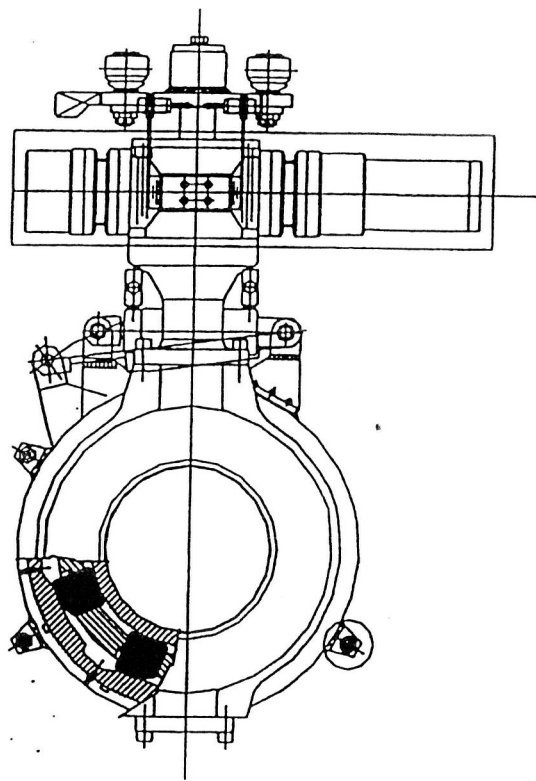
Fig. C: Vista frontale con dettaglio del sistema di bloccaggio
